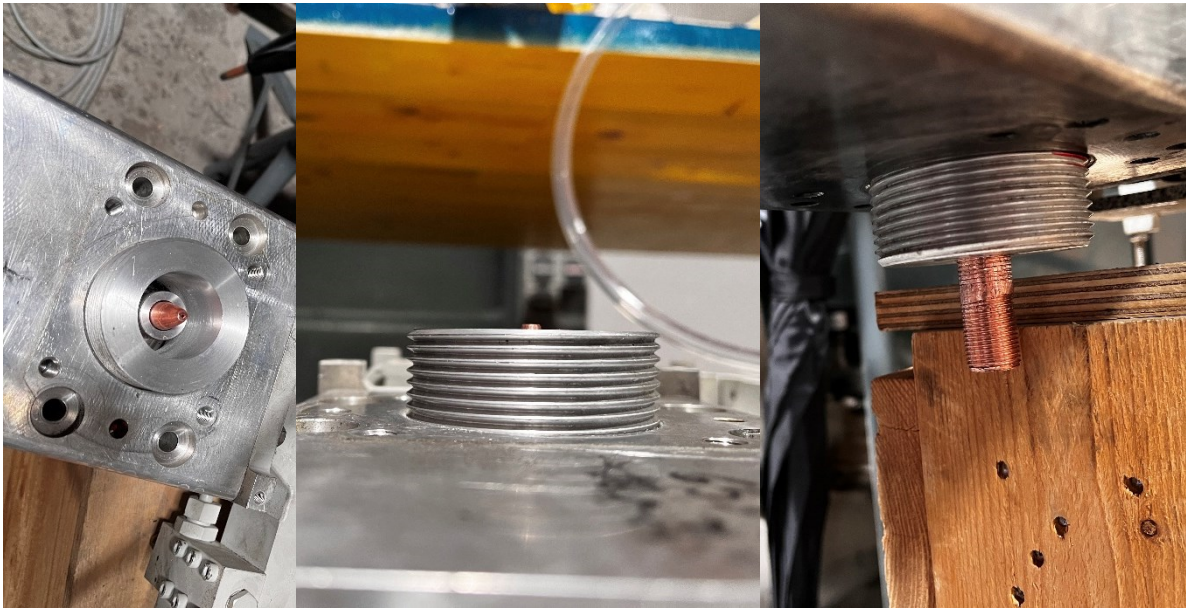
Kupferspitze mittels Aluminiumgehäuseschrauben verbaut im Aluminiumgehäuse von oben (links und mittig) und von unten (rechts)
